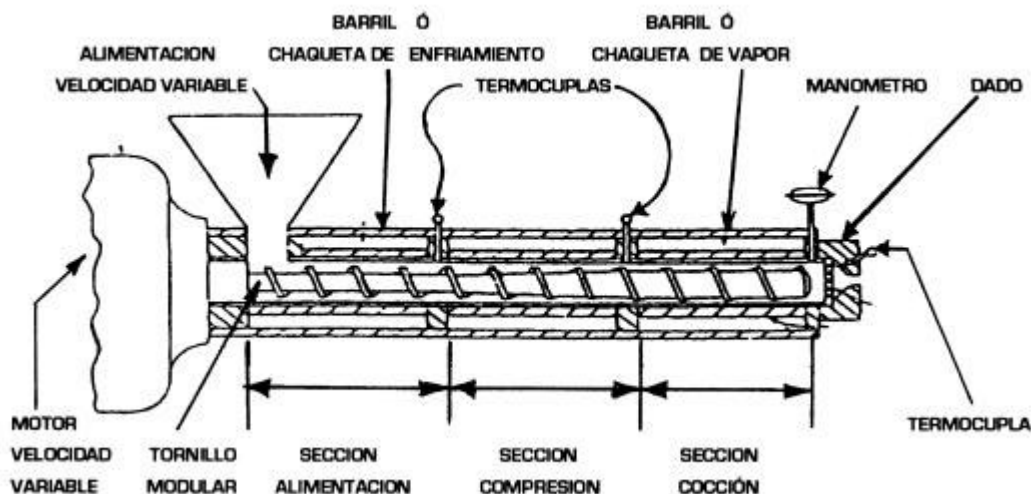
EXTRUSOR DE TORNILLO SIMPLE
